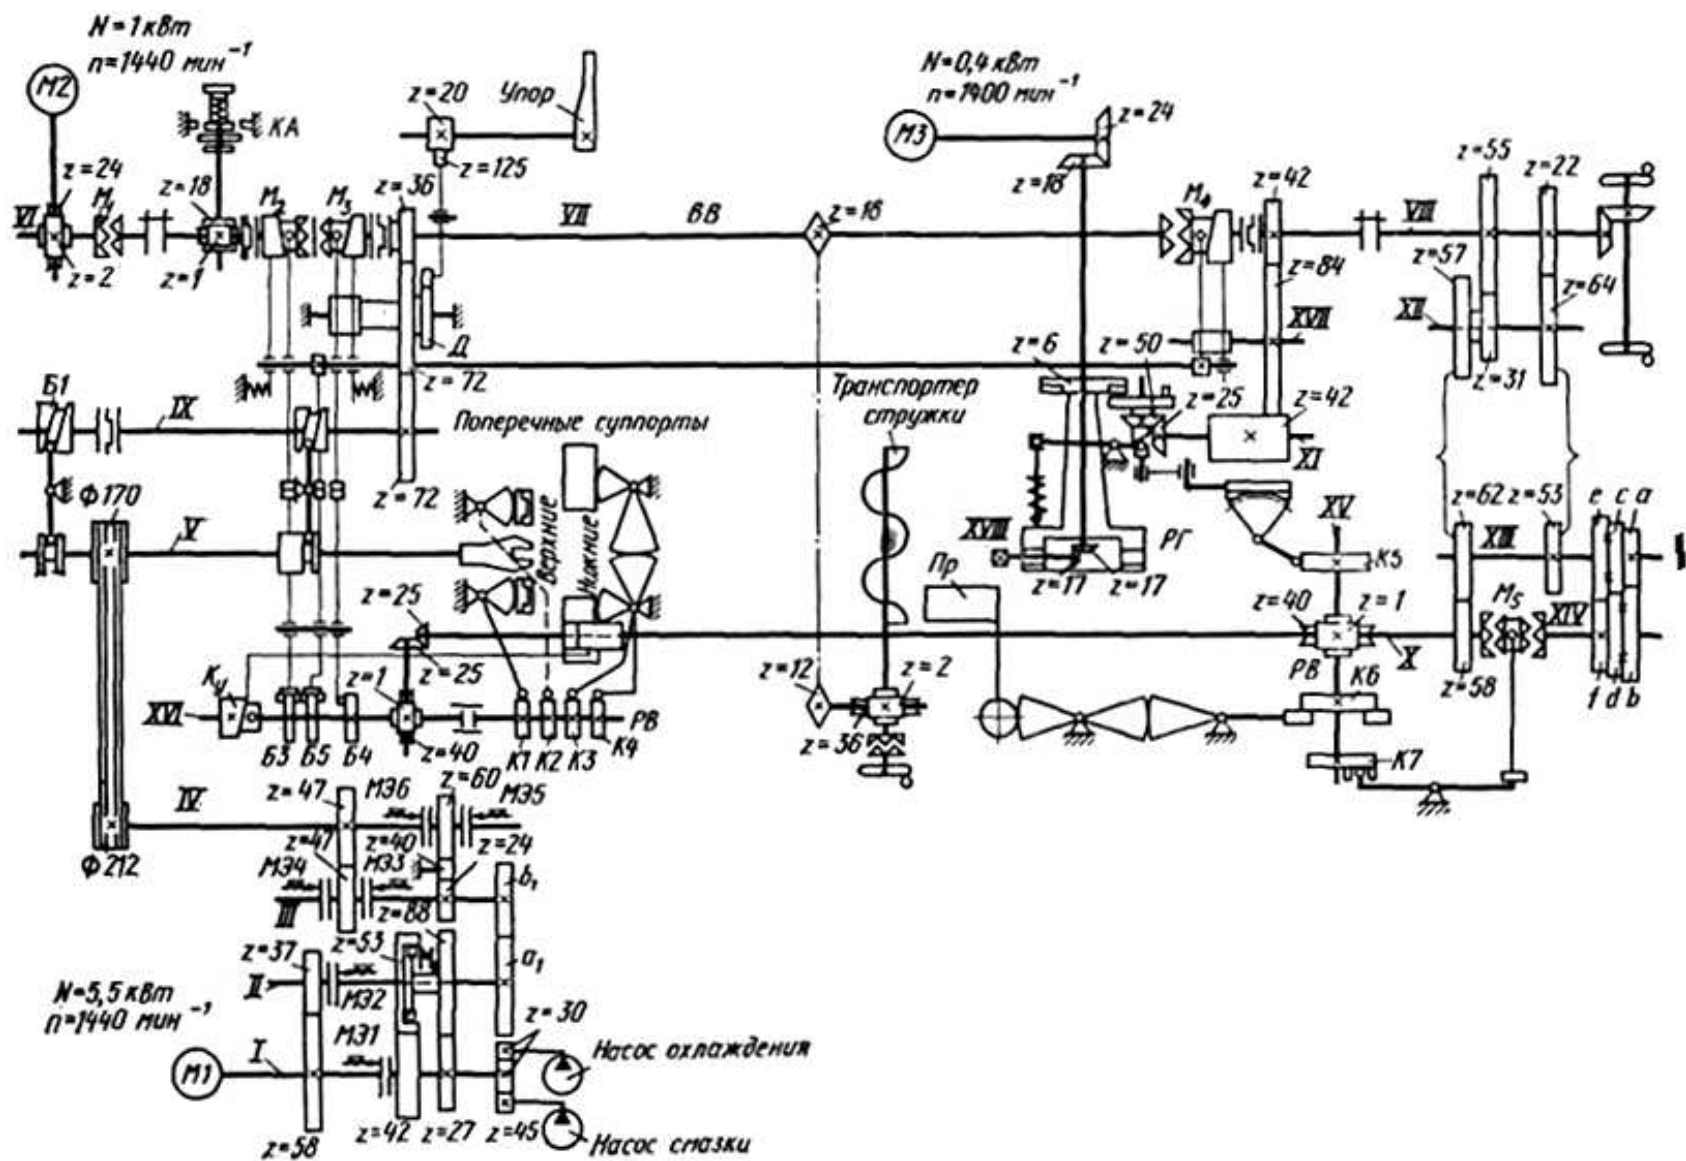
Кинематическая схема токарно-револьверного автомата
